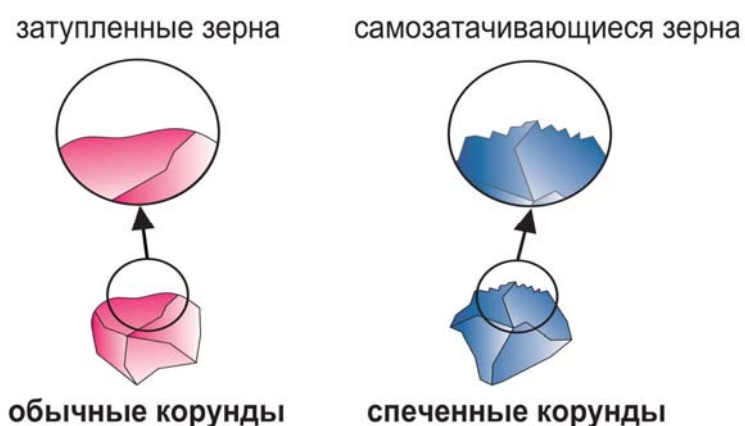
Поверхности режущих зерен из обычных и спеченных корундов
